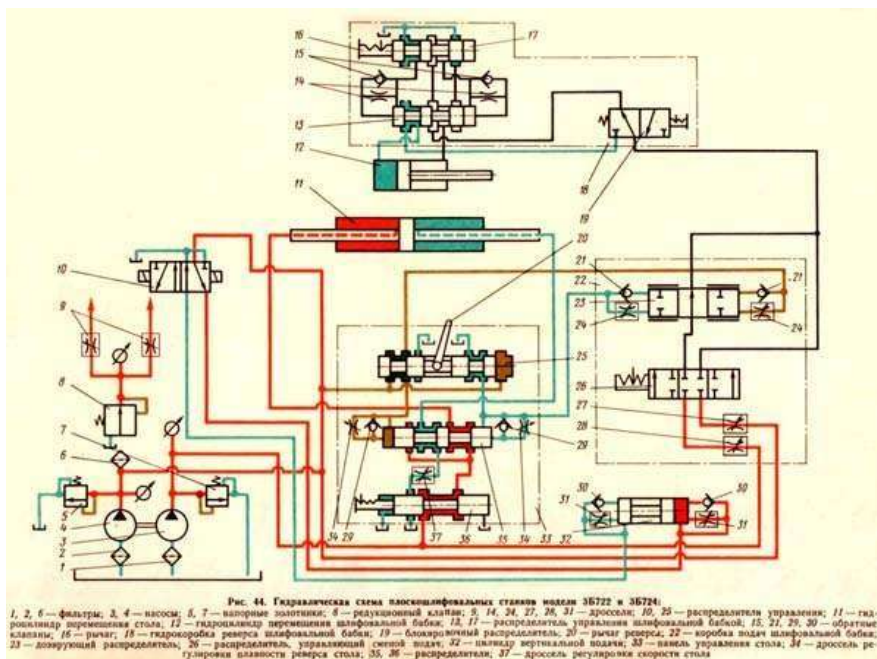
Схема гидравлическая плоскошлифовального станка 3Б722
